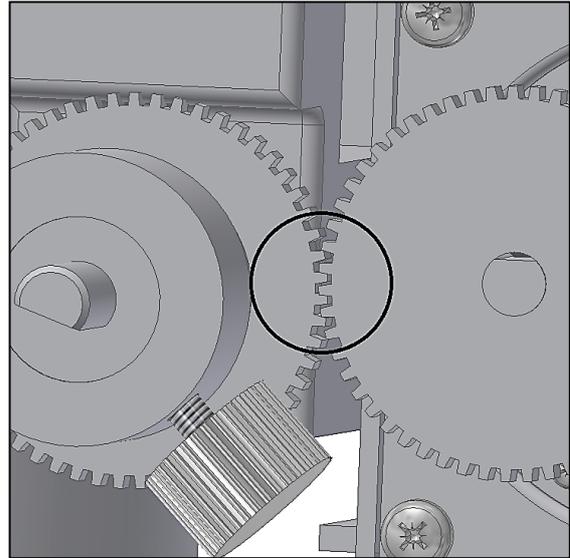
Bringen Sie die Zahnräder mit leichtem Spiel an.
